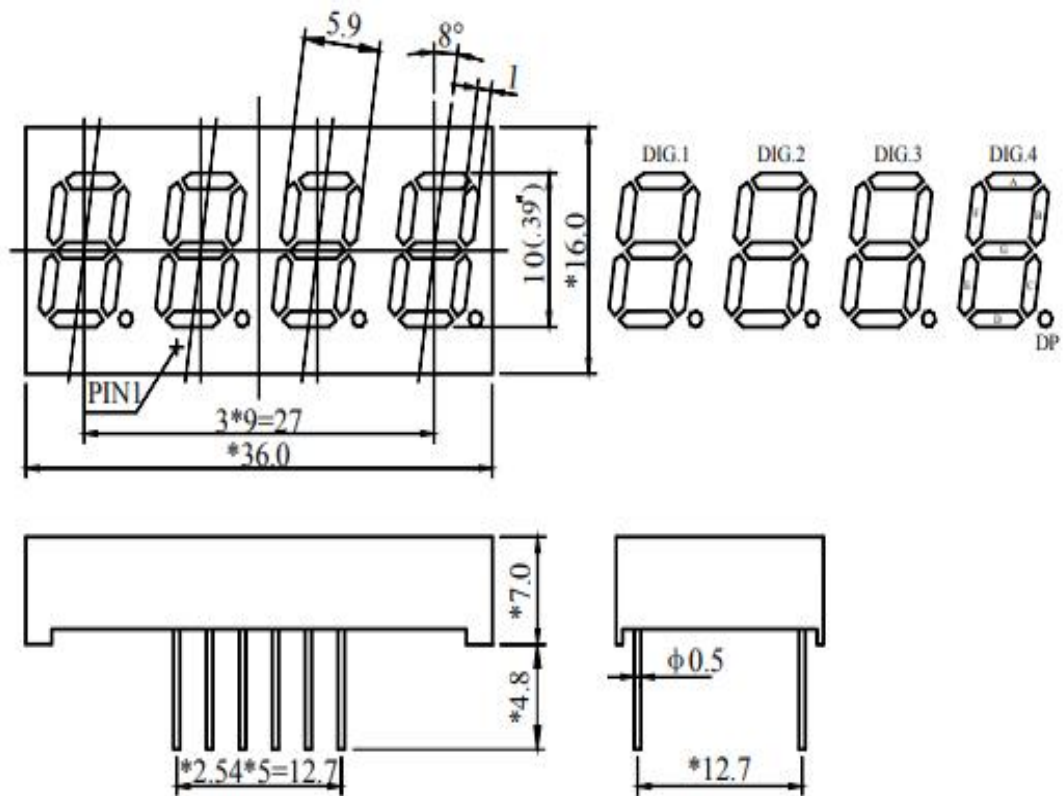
Габаритні розміри індикатора LFD039BAG-102-02
